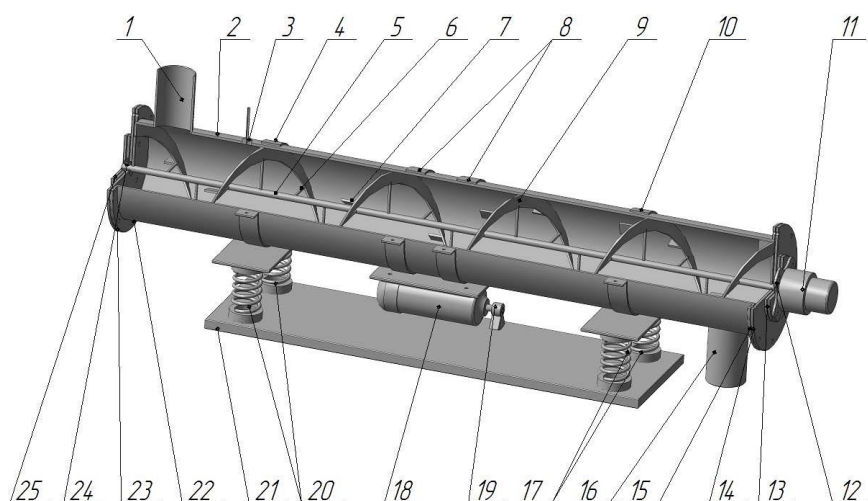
Барабанный виброгранулятор: 1 – загрузочный патрубок; 2 – обечайка; 3 – форсунка; 4, 10 – хомут опоры; 5 – вал; 6 – стержень; 7 – лопатка; 8 – хомут опоры вибровозбудителя; 9 – ленточная мешалка; 11 – двигатель привода ленточной мешалки; 12, 24 – подшипник скольжения; 13, 25 – крышка сквозная; 14, 23 – крышка; 15, 22 – фланец; 16 – разгрузочный патрубок; 17, 20 – пружина сжатия; 18 – двигатель вибровозбудителя; 19 – дебаланс; 21 – основание
